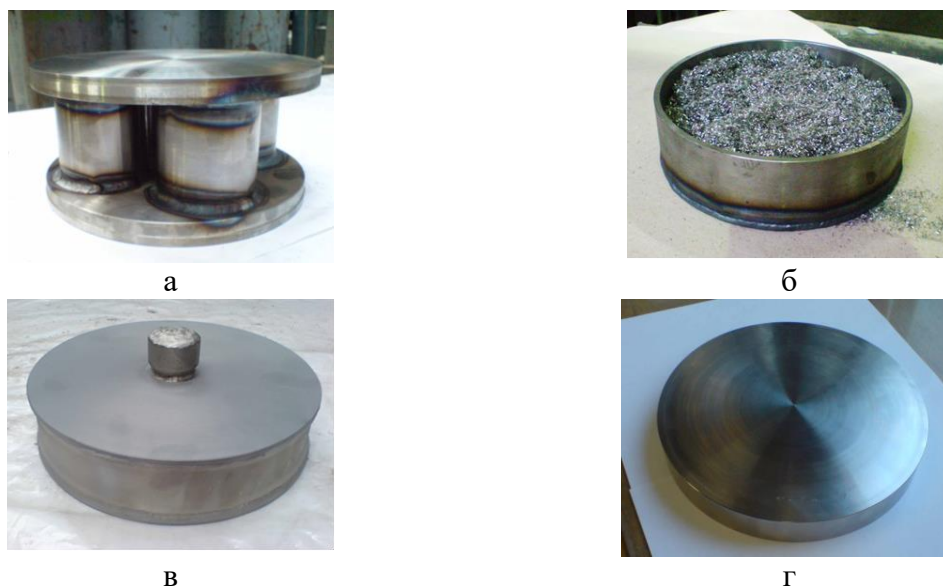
Внешний вид заготовки диска после различных этапов изготовления: а – толкатель для подпрессовки порошка в капсулу диска; б – порошок ПЧФ в капсуле диска; в – капсула диска после заварки; д – готовая экспериментальная заготовка диска
